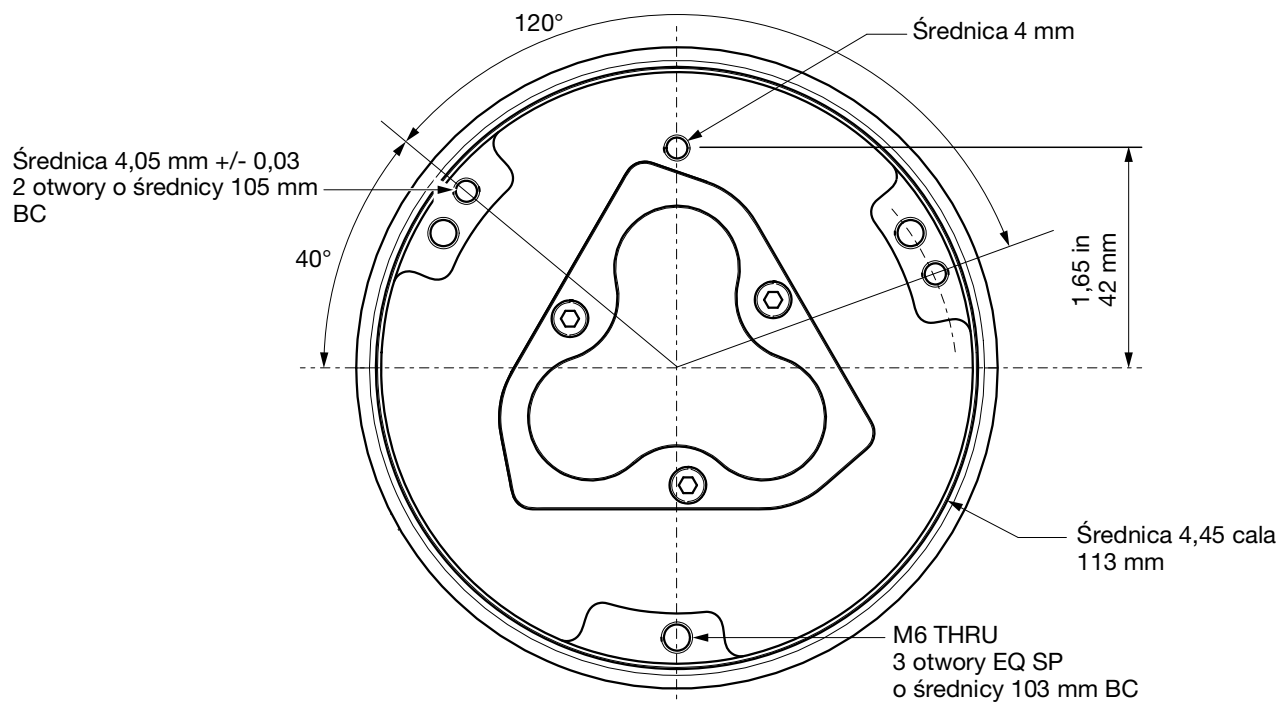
Kołnierz montażowy do robotów, typowy dla wszystkich pistoletów Switch 3D
